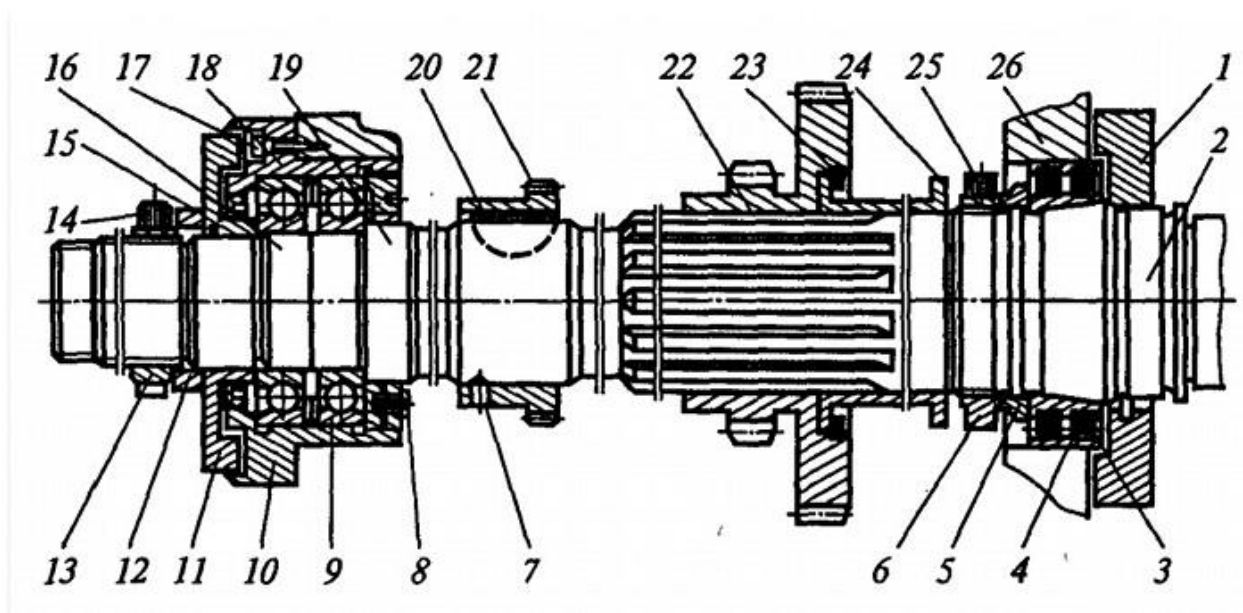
Шпиндельный узел токарно-винторезного станка:
